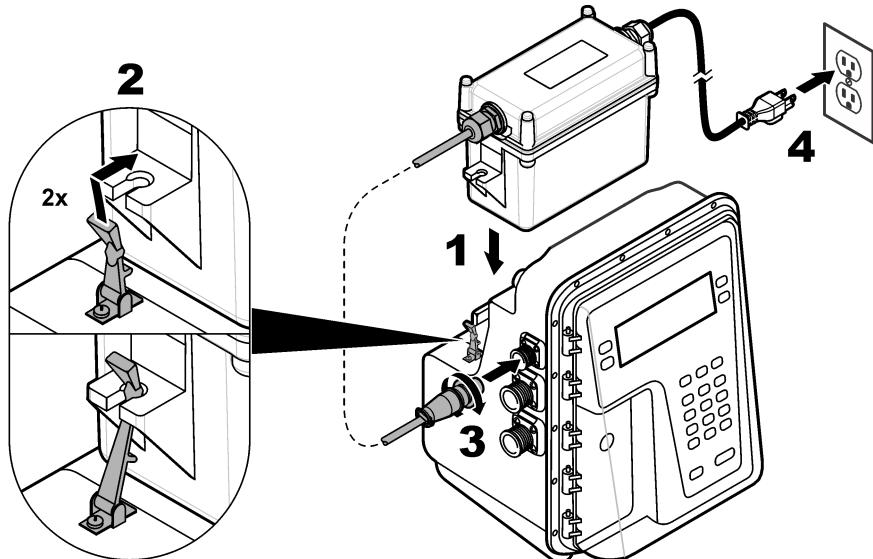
Installation auf einem gekühlten Probenehmer
